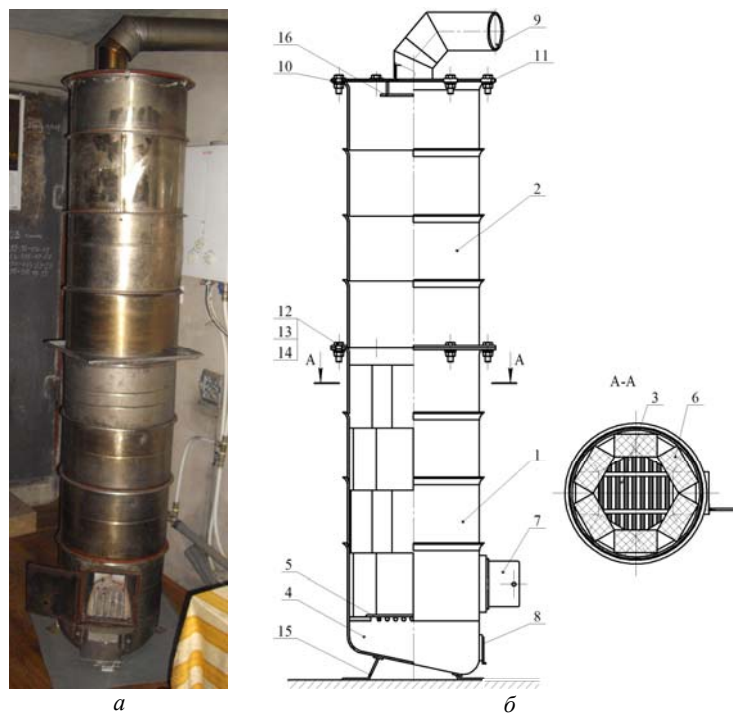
Піч дров'яна періодичного функціонування: *а* – вигляд загальний; *б* – конструктивна схема: 1 – корпус нижній футерований; 2 – корпус верхній; 3 – камера згоряння; 4 – зольник; 5 – решітка колосникова; 6 – цегла вогнетривка; 7 – дверцята завантажувального отвору; 8 – заслінка піддувала; 9 – труба вентиляційна; 10 – кришка; 11 – скоба; 12 – болт; 13 – шайба; 14 – гайка; 15 – ніжки; 16 – екран
